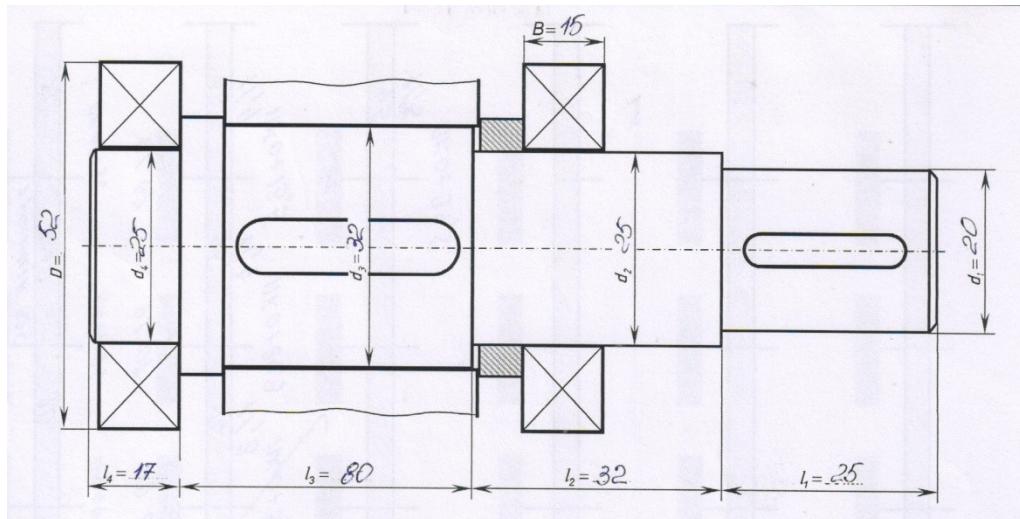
Конструкция тихоходного вала цилиндрического редуктора.
